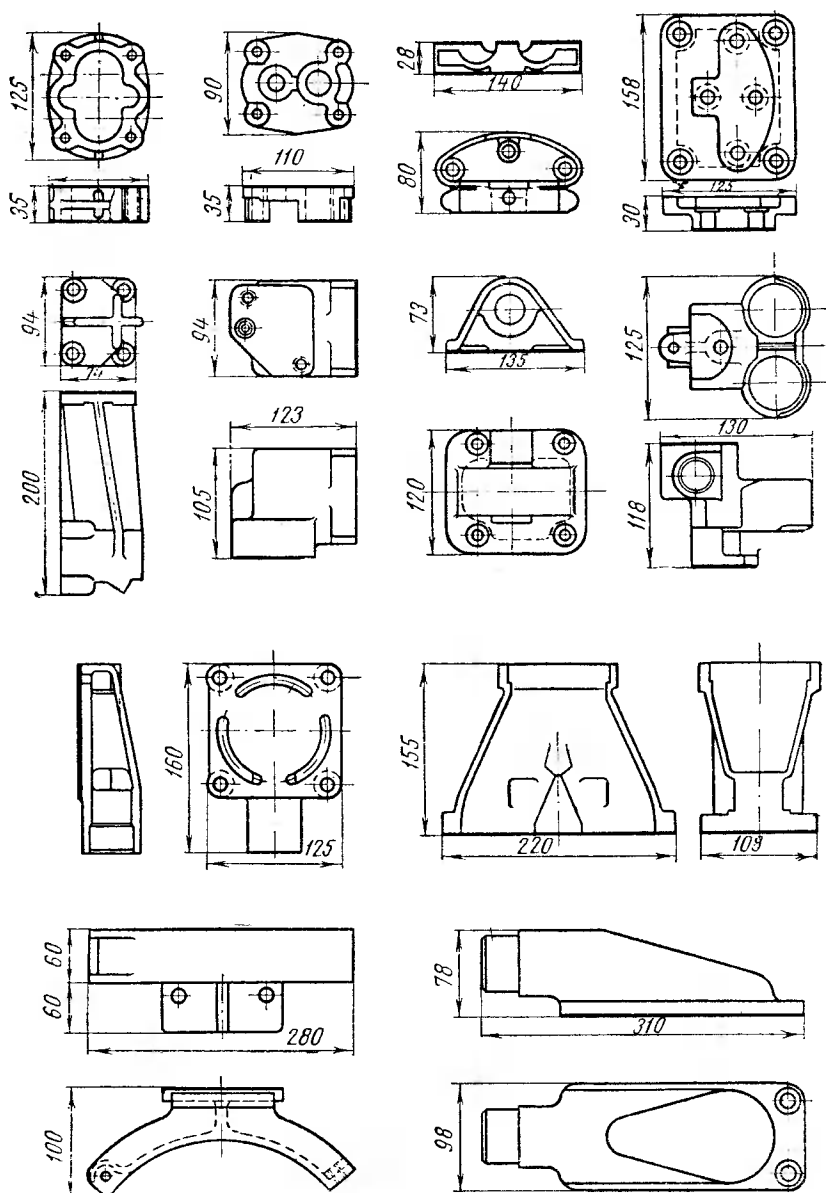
Чугунные детали, обрабатываемые протяжкой из твердого сплава на станке 7Б720
